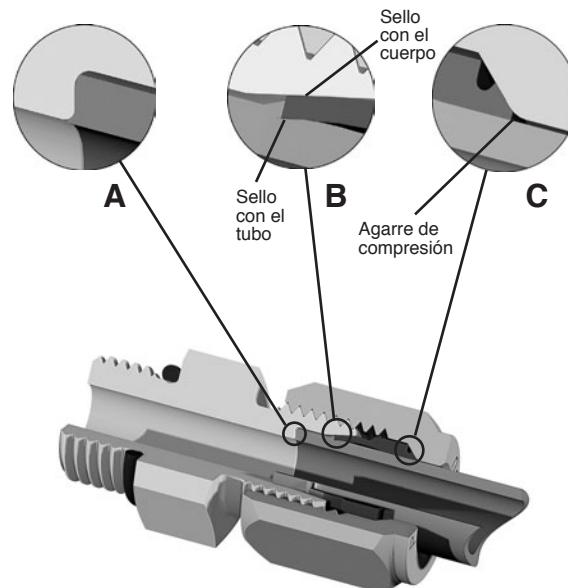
Conexión Ferulok Ensamblado con Tubo
